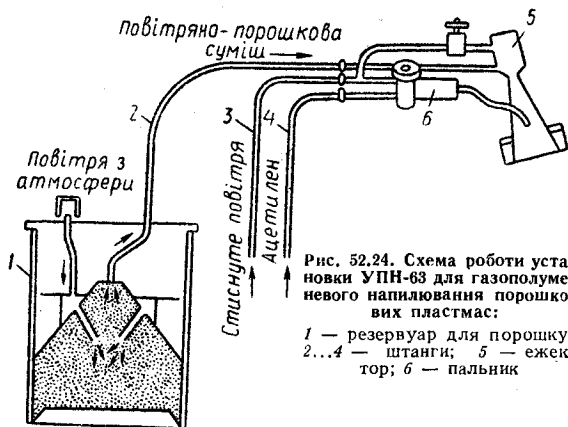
Схема роботи установки УПН-63 для газополум'яного наповнення порошкових пластмас:
